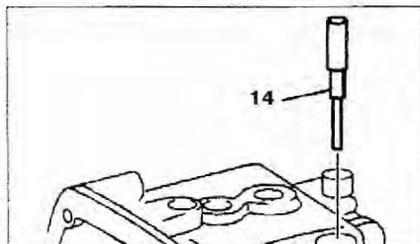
Снимите плунжер 14 из корпуса коробки передач.
